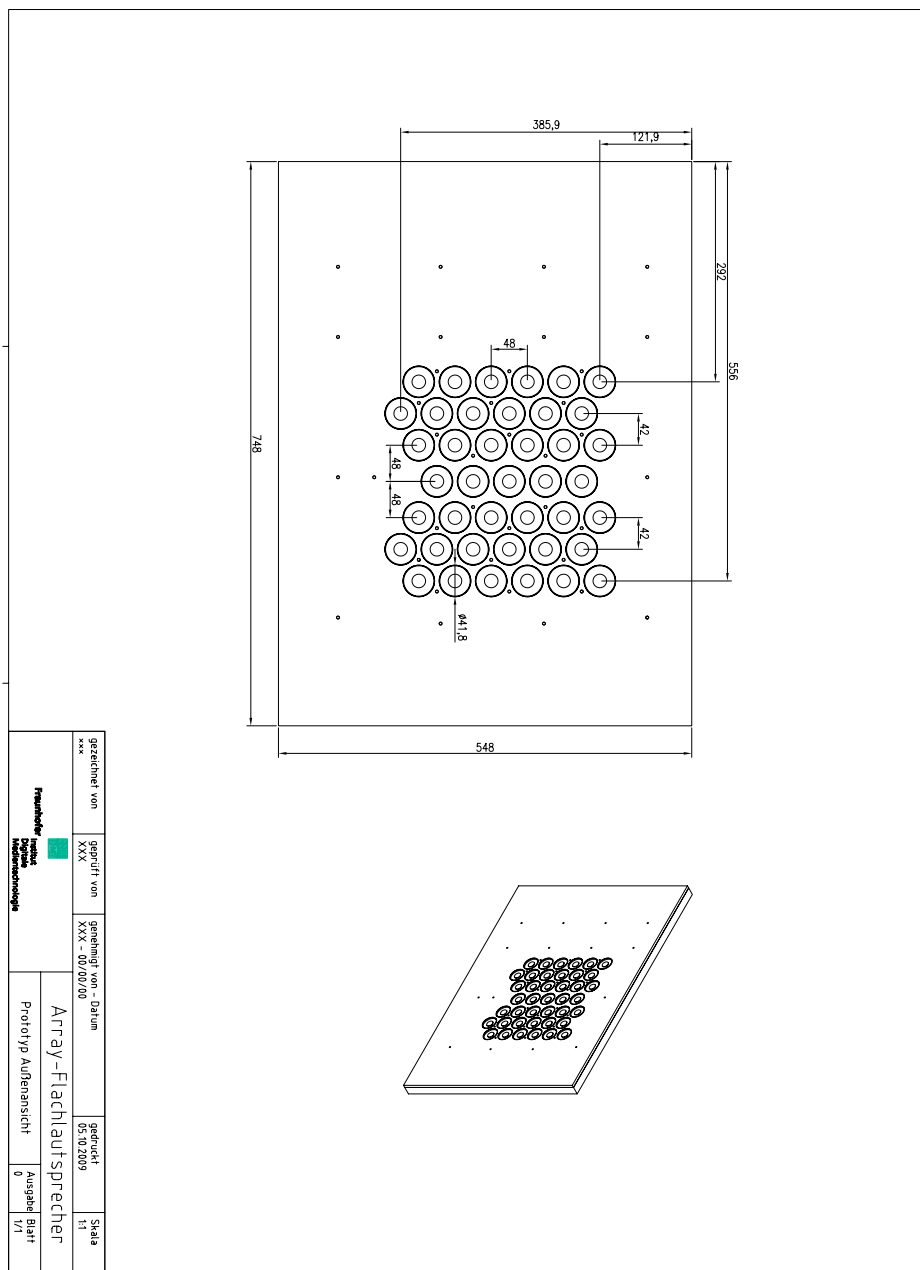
Konstruktionszeichnung des gefertigten Flachlautsprechers in der Draufsicht
